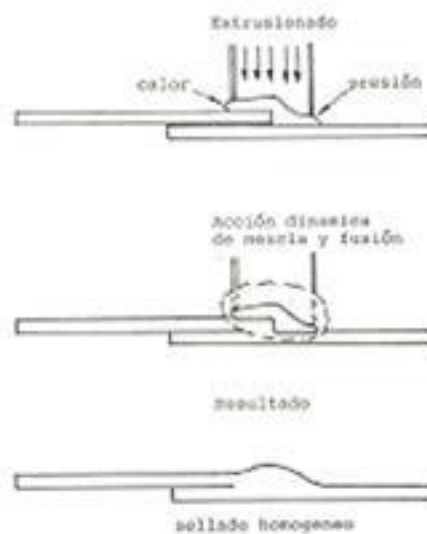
Fusión con aporte de material en caliente (soldadura por extrusión)
